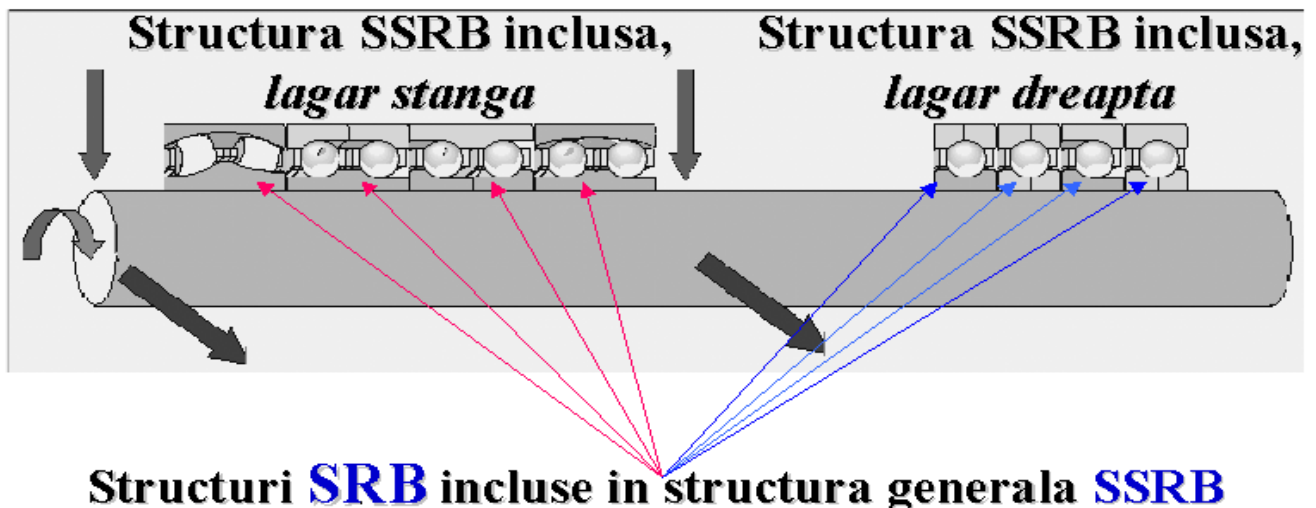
Elemente componente ale unei suprastructuri SSRB
